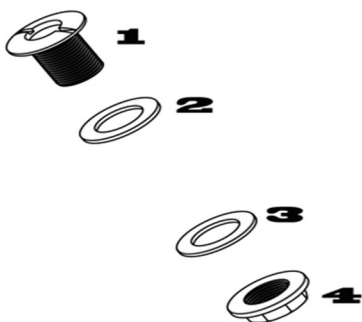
Durchführung oder Tankverschraubung (die Glasscheibe befindet sich zwischen Gleitring 3 und Gummiring 2)
